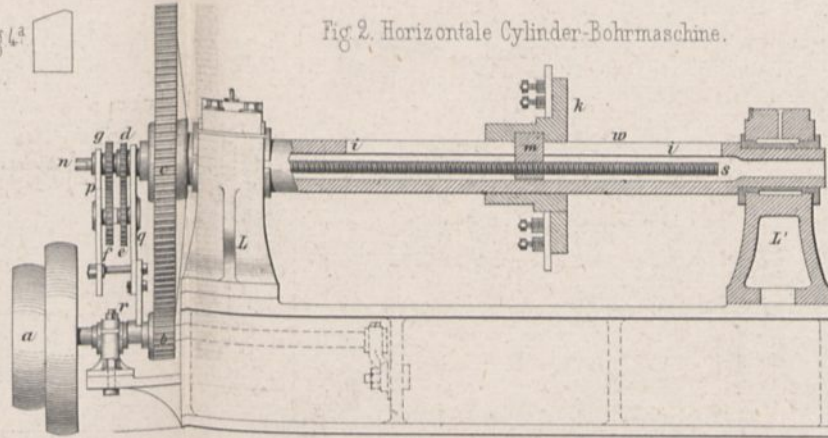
Horizontale Cylinder-Bohrmaschine.
